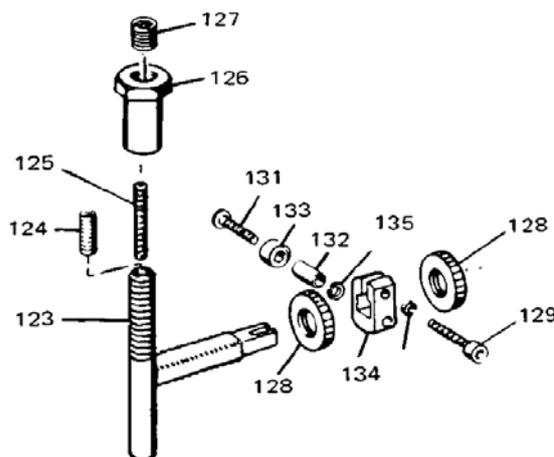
Покомпонентный чертеж регулировки высокой скорости
